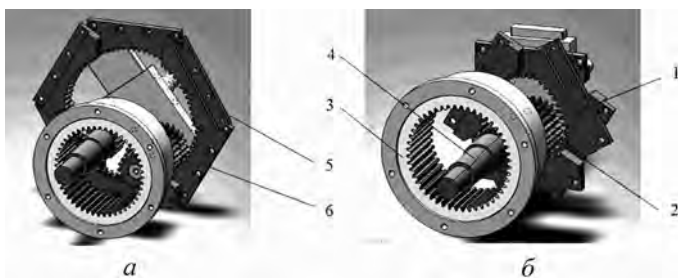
Принципиальная схема планетарной плавнорегулируемой передачи: *а* – положение деталей передачи при минимальном передаточном отношении; *б* – положение деталей передачи при максимальном передаточном отношении: 1 – сектор центрального зубчатого колеса одного силового потока, 2 – двухпоточный сателлит, 3 – устройство для передачи вращения сателлита ведомому валу, 4 – выходной вал, 5 – входной вал, 6 – составное полисекторное (центральное) зубчатое колесо
